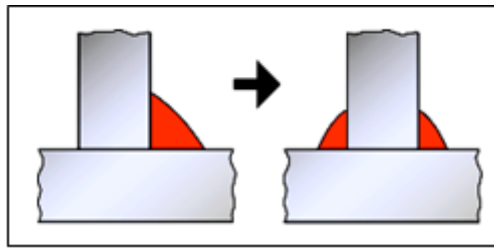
Configuration du Joint, plus petites soudures d'angle à deux faces. [12]
